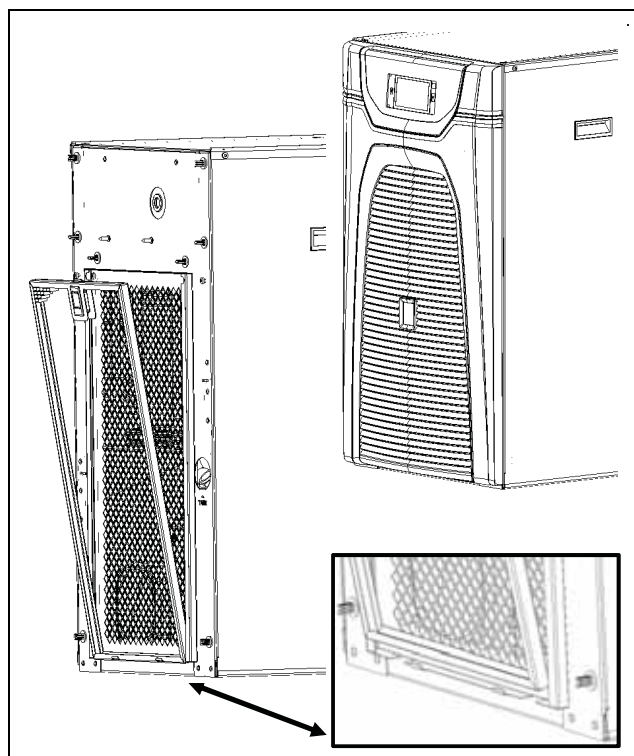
Установка металлического фильтра 3320200 и 3334300
